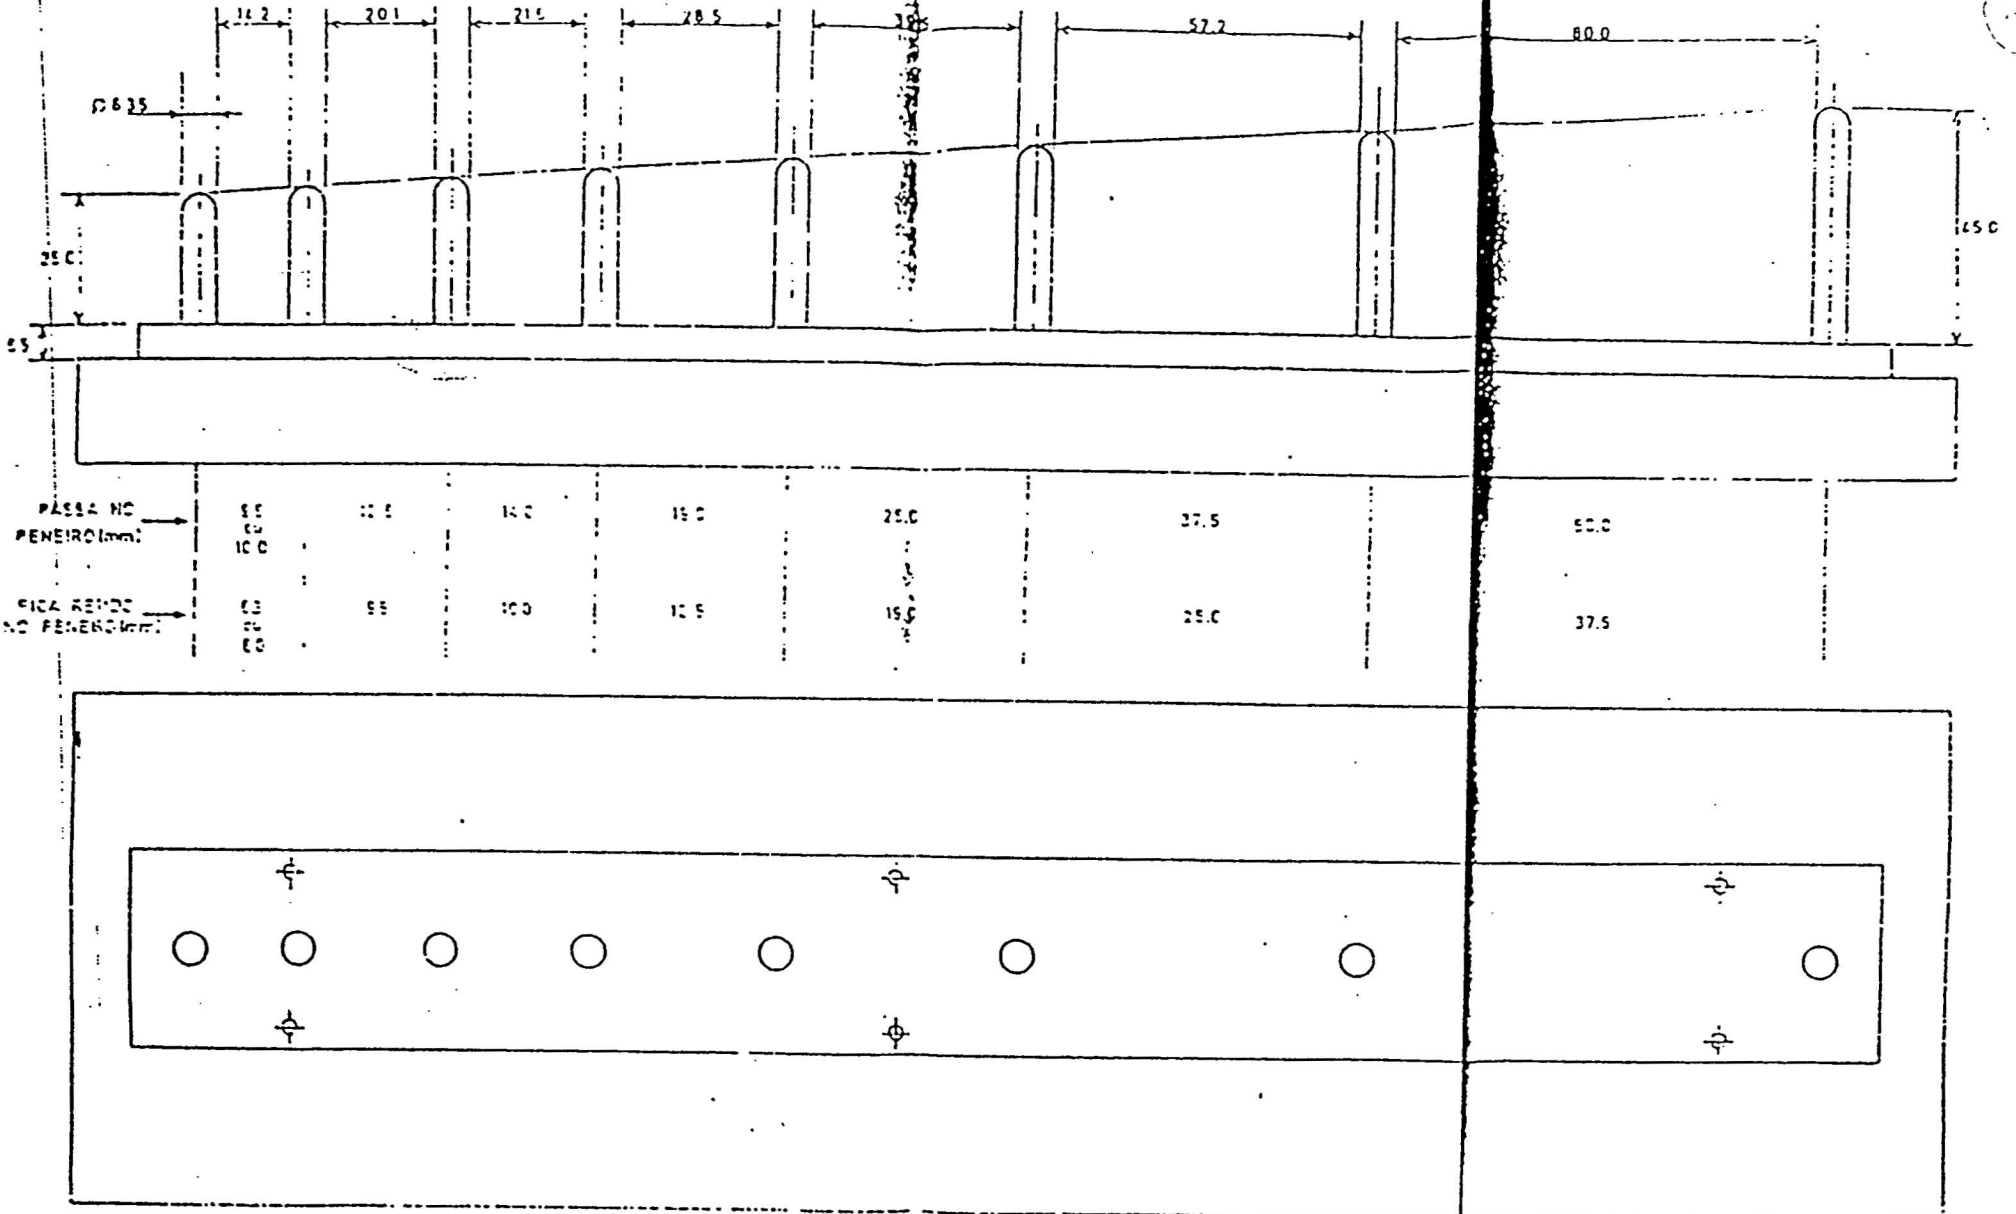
MEDIDOR DE COMPRIMENTOS (em mm)
